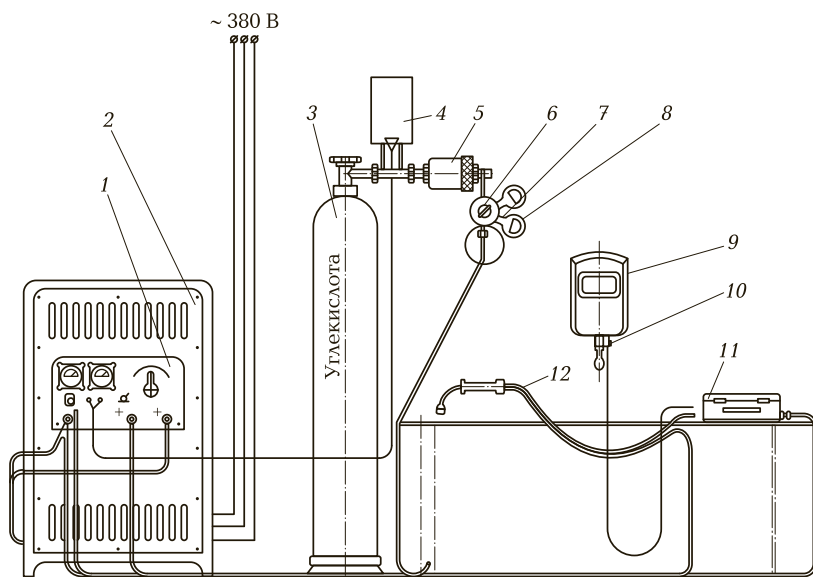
Схема поста А-547Р для полуавтоматической сварки в среде углекислого газа проволокой диаметром 0,8...1,0 мм:
